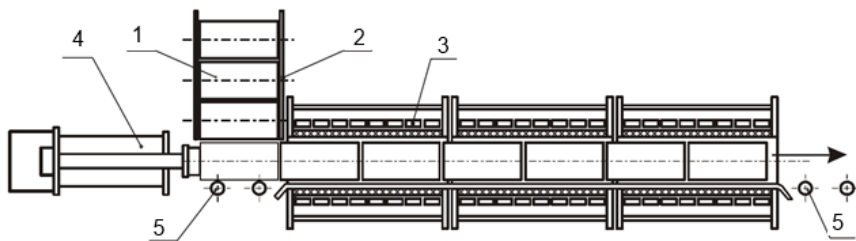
Общий вид индукционного нагревателя: 1 – заготовки; 2 – бункер; 3 – индуктор; 4 – толкатель; 5 – ролики транспортера.
